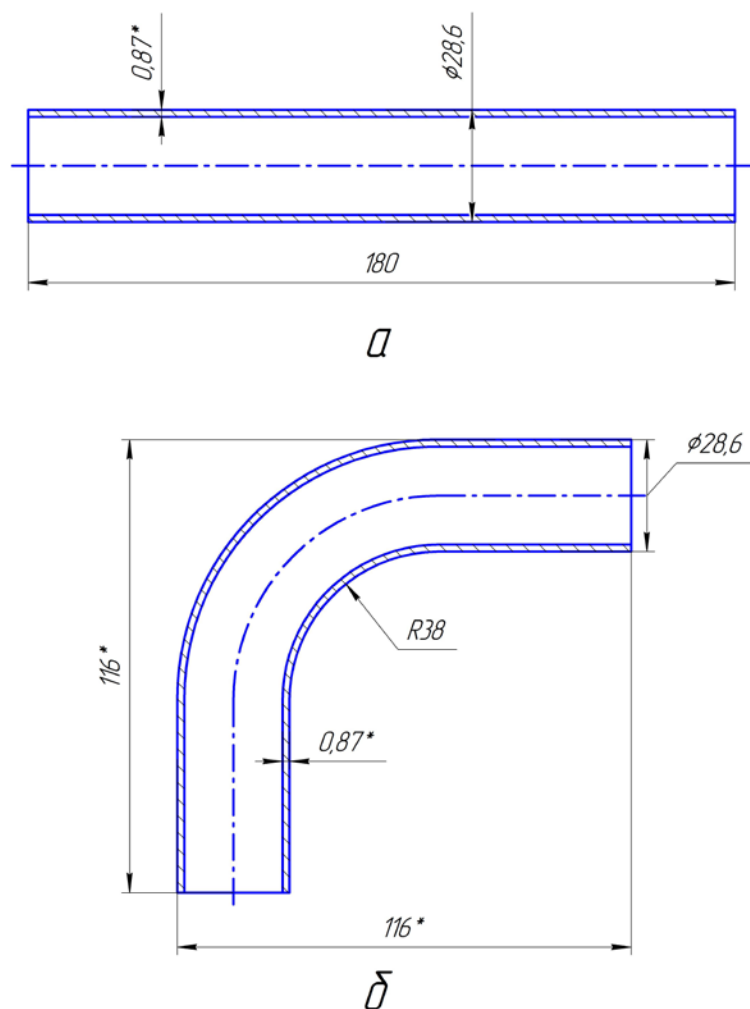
Эскизы исходной заготовки (а) и заготовки после гибки (б)
